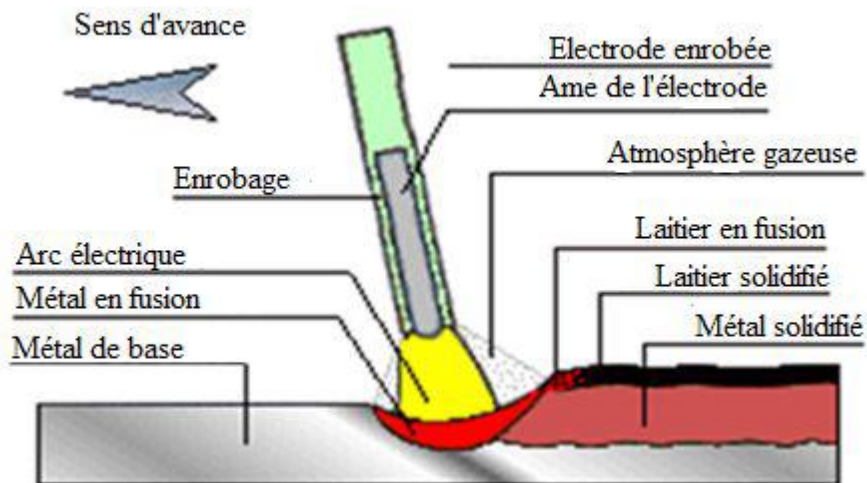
Soudage à arc à l'électrode enrobée
